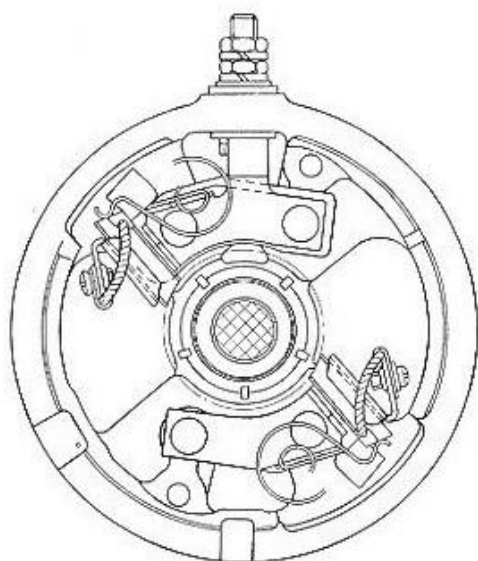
Querschnitt durch die Lichtmaschine und Ansicht des Kollektorlagers.
